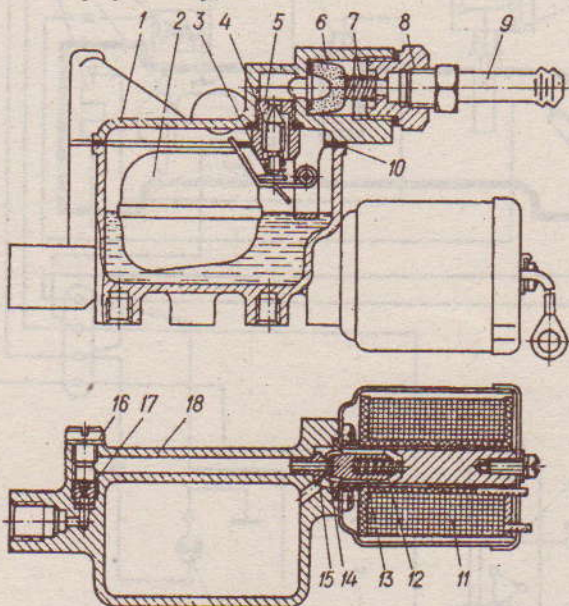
Регулятор подачи топлива: 1 - крышка поплавковой камеры; 2 - поплавок; 3 - пружина; 4 - игла запорная; 5 - седло; 6 - фильтр; 7 - пружина фильтра; 8 - гайка; 9 - штуцер; 10 - прокладка; 11 - катушка клапана; 12 - пружина; 13 - клапан; 14 - прокладка клапана; 15 - седло клапана; 16 - пробка; 17 - жиклер; 18 - корпус поплавковой камеры
